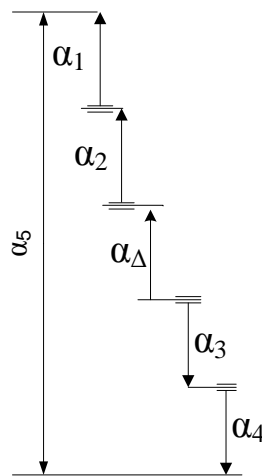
Схема розмірного ланцюга технологічної системи, який визначає поворот поверхні оброблюваної деталі відносно осі обертання шпинделя
